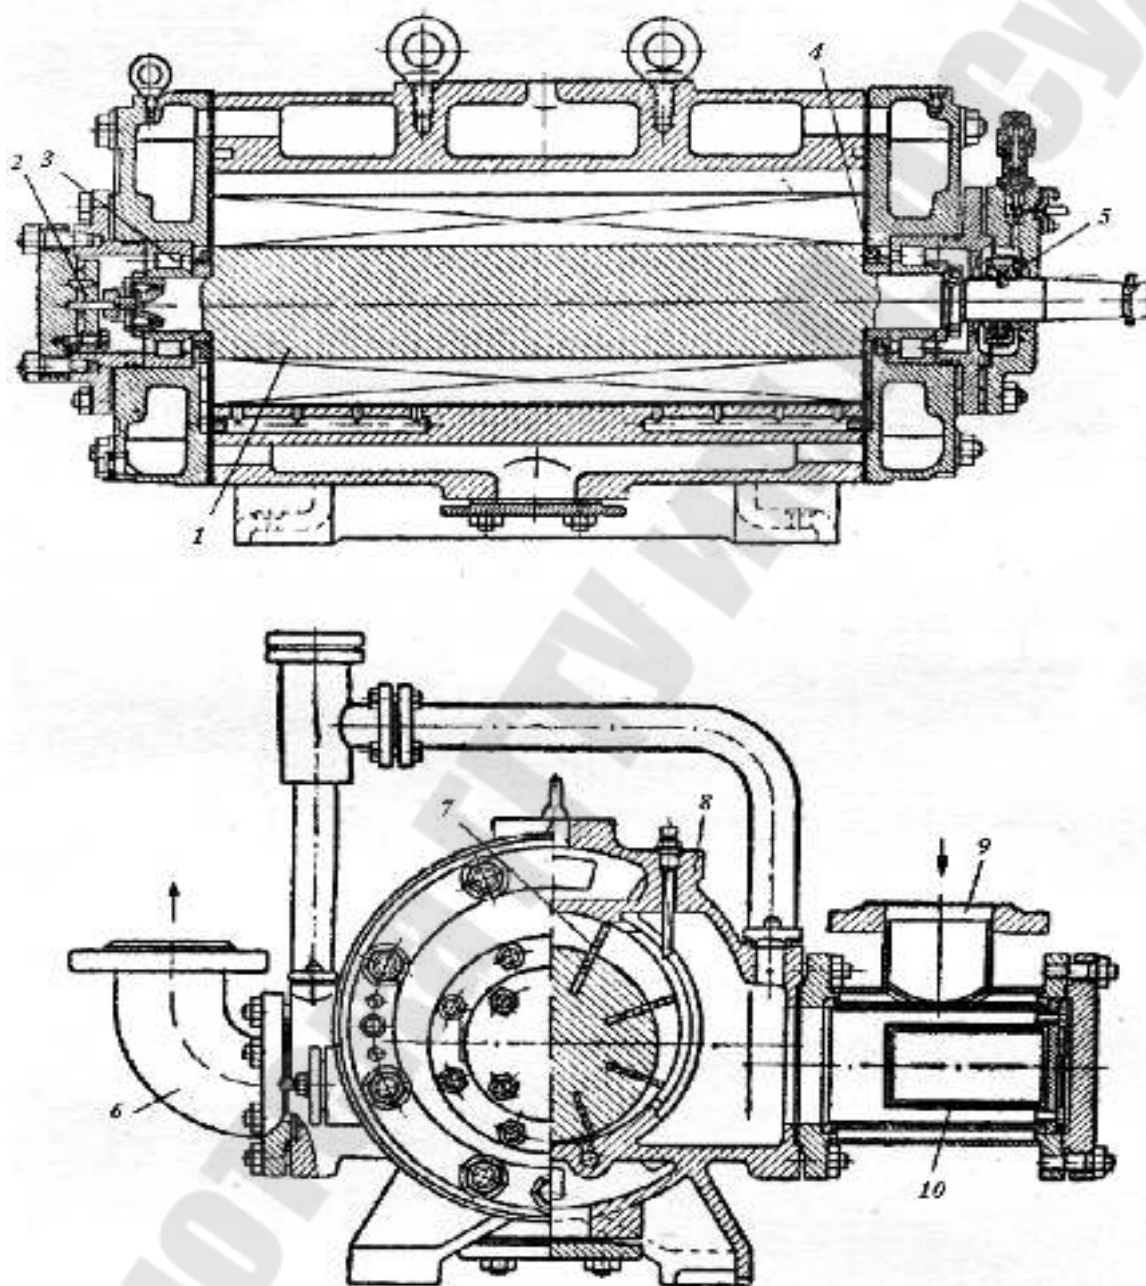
[13]. Пластинчатый ротационный компрессор: 1 – ротор; 2 – шестеренчатый насос; 3 – подшипники; 4 – асботекстолитовые кольца; 5 – сальник; 6 – нагнетательный патрубок с обратным клапаном; 7 – асботекстолитовые пластины; 8 – цилиндр; 9 – всасывающий патрубок; 10 – газовый сетчатый фильтр
